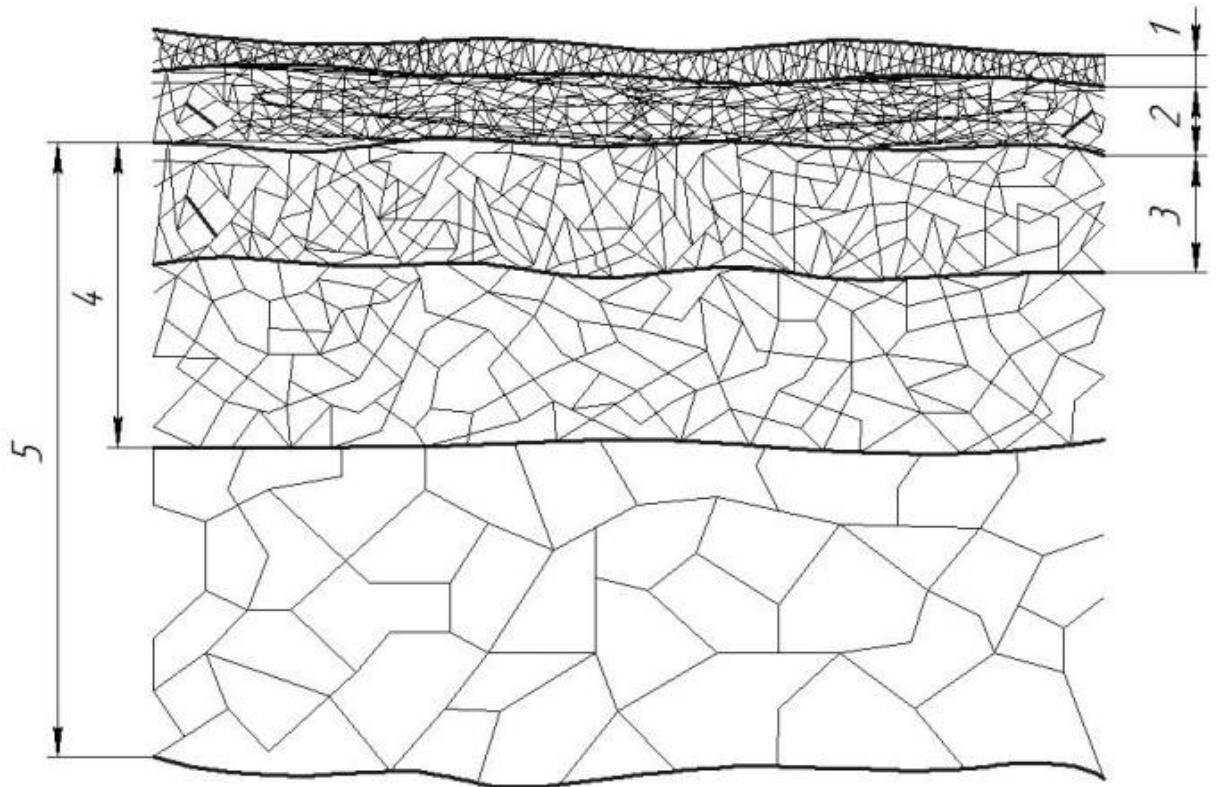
Схематичне розташування зон поверхневого шару, що піддався електроерозійній обробки
